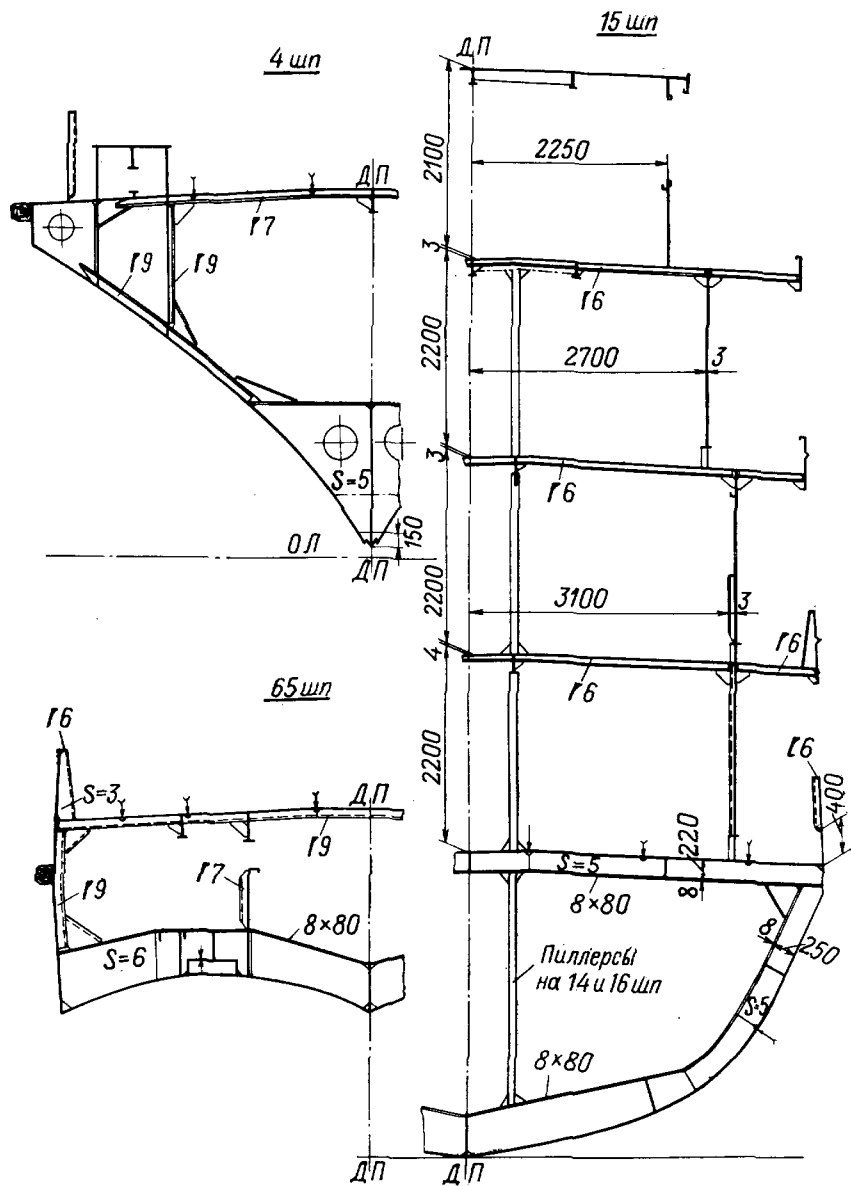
Конструктивные сечения корпуса толкача-буксира ОТА-852.
